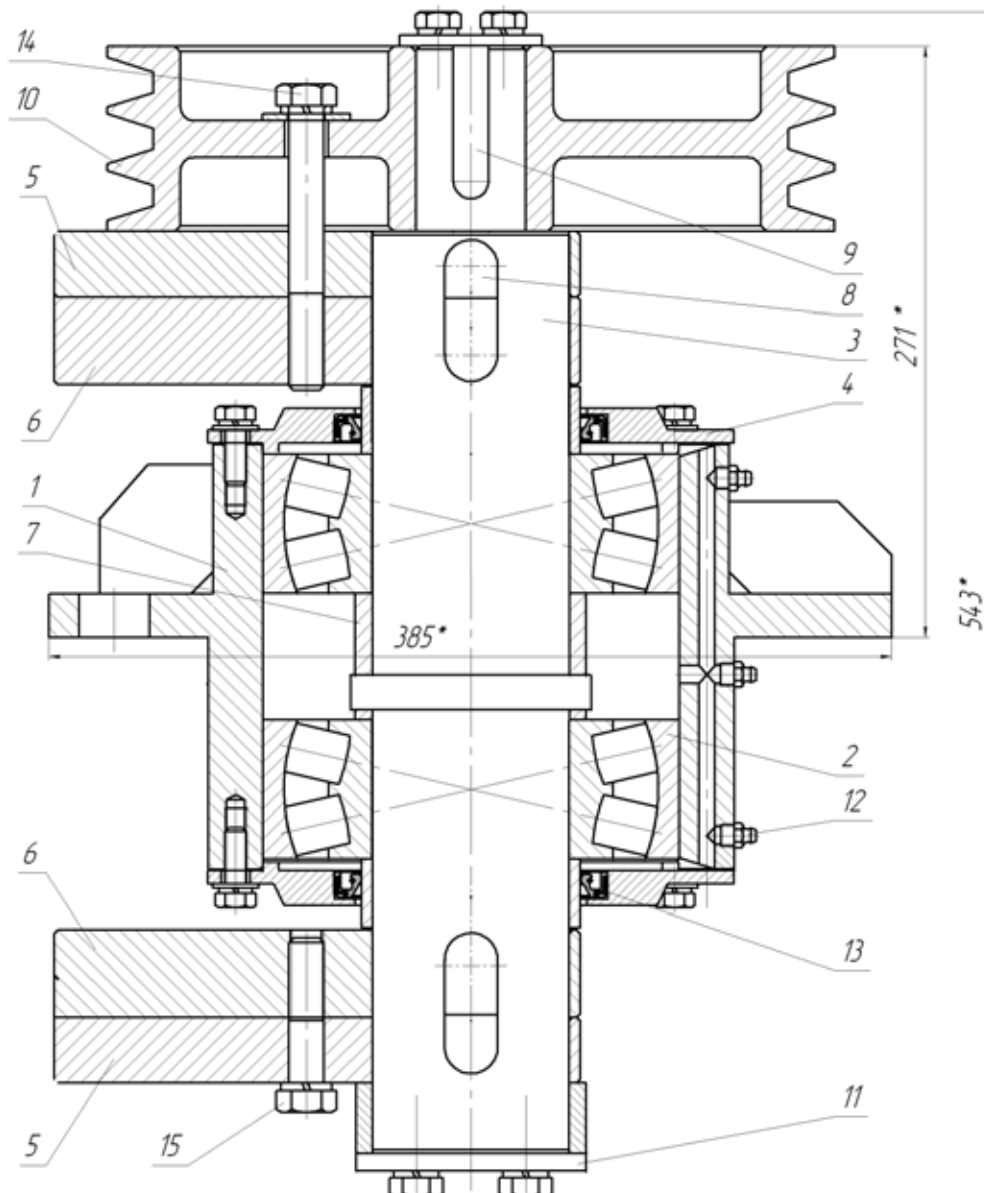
Низькочастотний вібраційний збудник коливань: 1 – корпус; 2 – підшипник; 3 – вал; 4 – кришка підшипника прохідна; 5 – дебаланс, що повертається на валу; 6 – нерухомий дебаланс; 7 – розпірна втулка; 8 – спеціальна шпонка; 9 – шпонка; 10 – шків; 11 – торцева шайба; 12 – масленичка; 13 – манжета; 14, 15 – регулювальні болти
